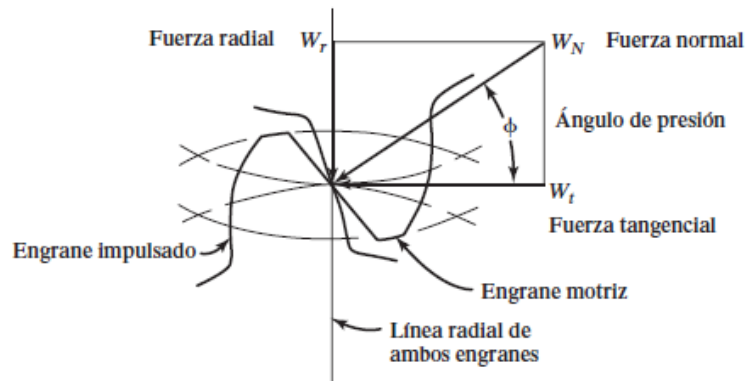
Fuerzas sobre los dientes de un engranaje [24].
